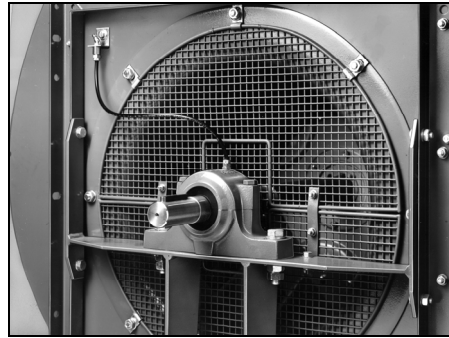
Steh-Gussgehäuse mit Pendelkugellager
